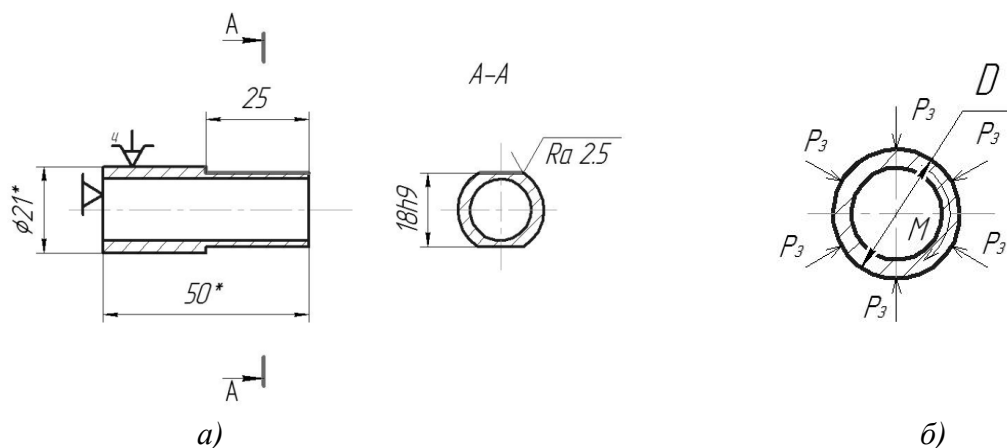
Установка заготовки в цанговый патрон с упором в торец:
